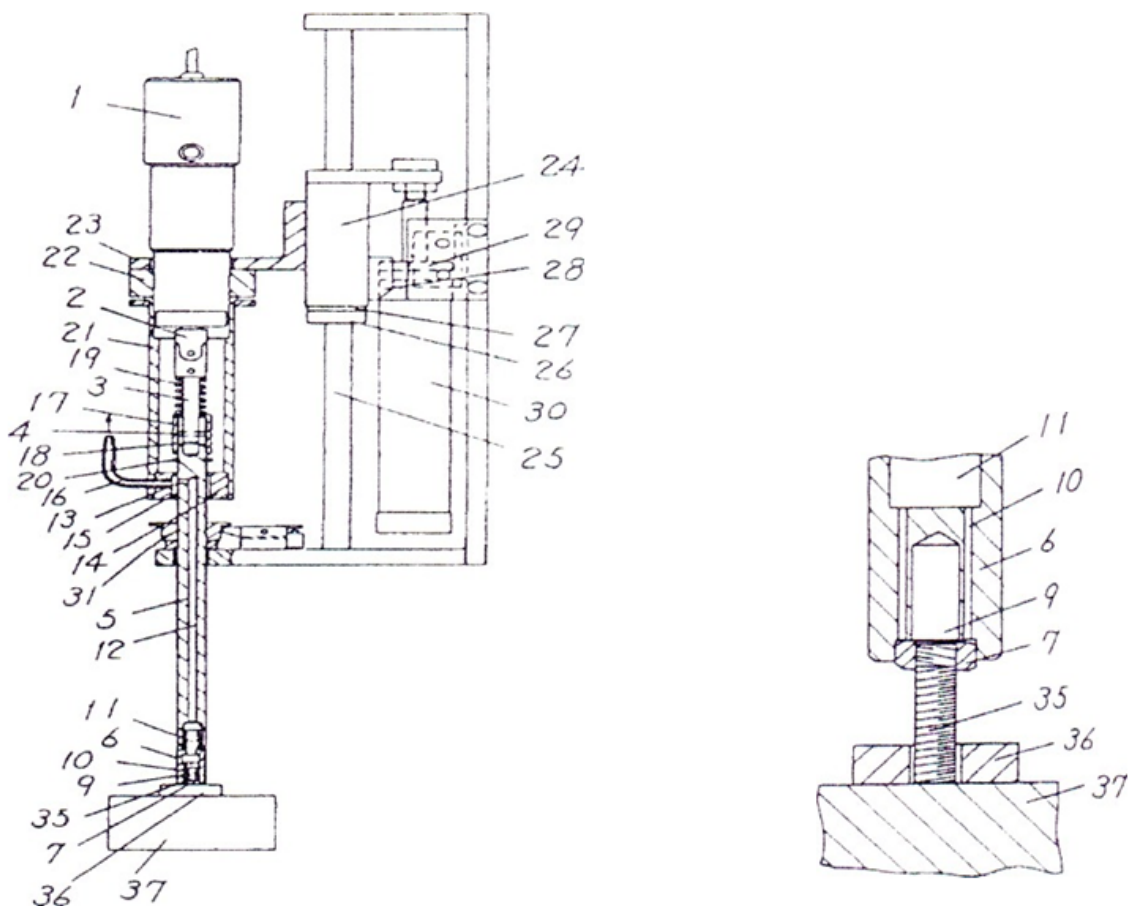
Автоматичний пристрій для загвинчування гайок: 1- електропривод; 5- шпindelь; 6- головка; 7- нагвинчувана гайка; 10, 11, 12- повітрянi канали; 16- відсмоктувальний штуцер; 35- шпилька.
